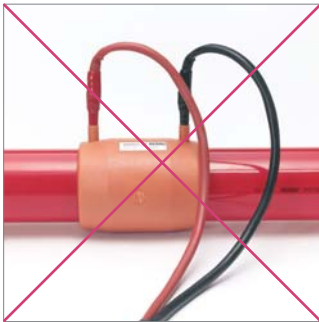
Rohre nicht ohne montierte Universalrohrhalteklammern verschweißen.
